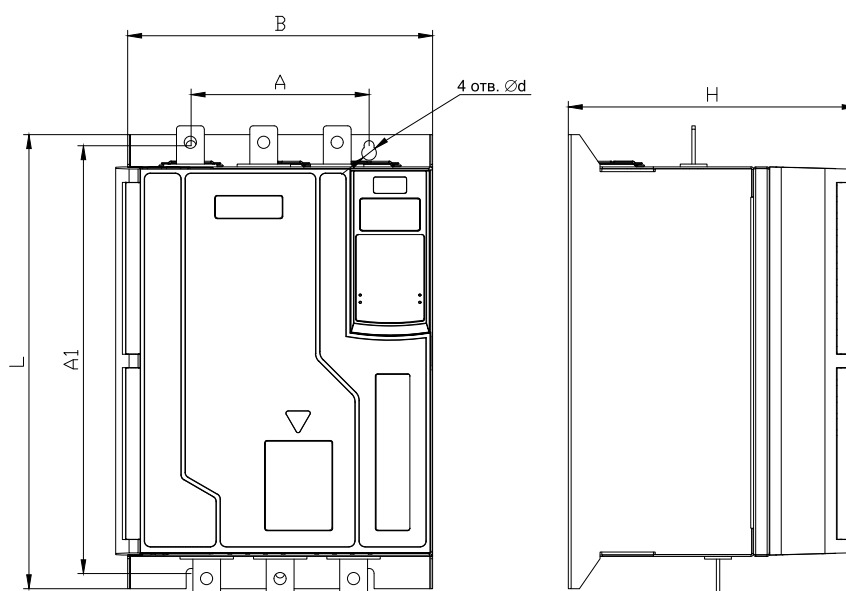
Габаритные и установочные размеры УПП, габарит 2
